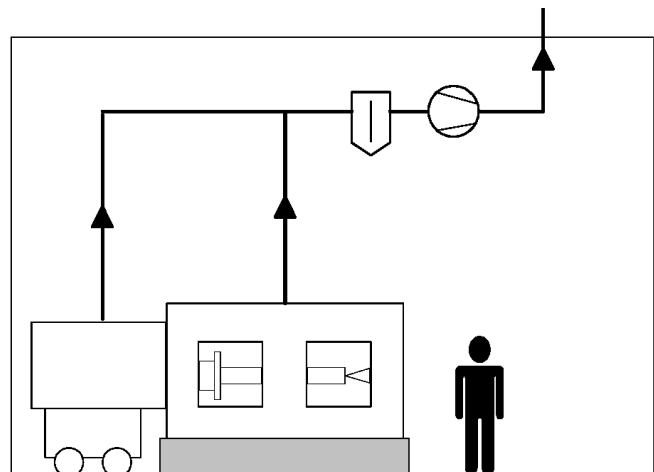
Beispiel für eine eingehauste Werkzeugmaschine.
